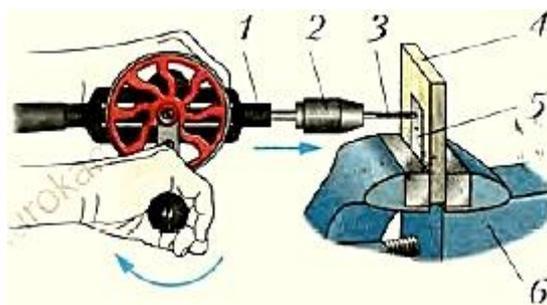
Сверление отверстий в заготовке, закреплённой в тисках: 1 — дрель; 2 — патрон; 3 — сверло; 4 — деревянная дощечка; 5 — заготовка; 6 — тиски
